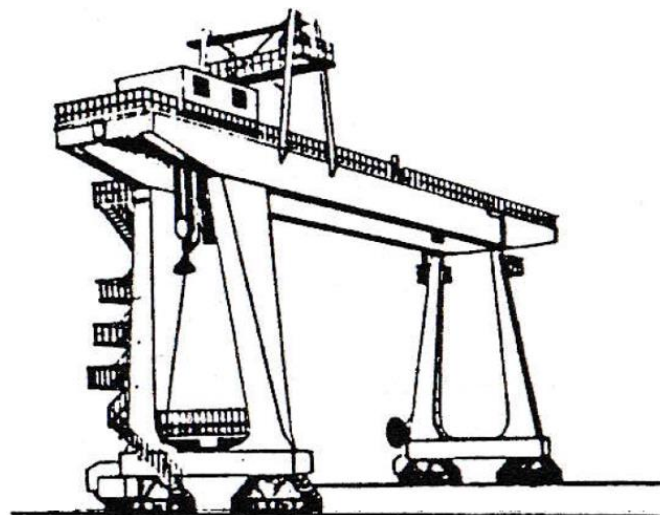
Grúa pórtico para elevadas cargas (10) (p. 265)
